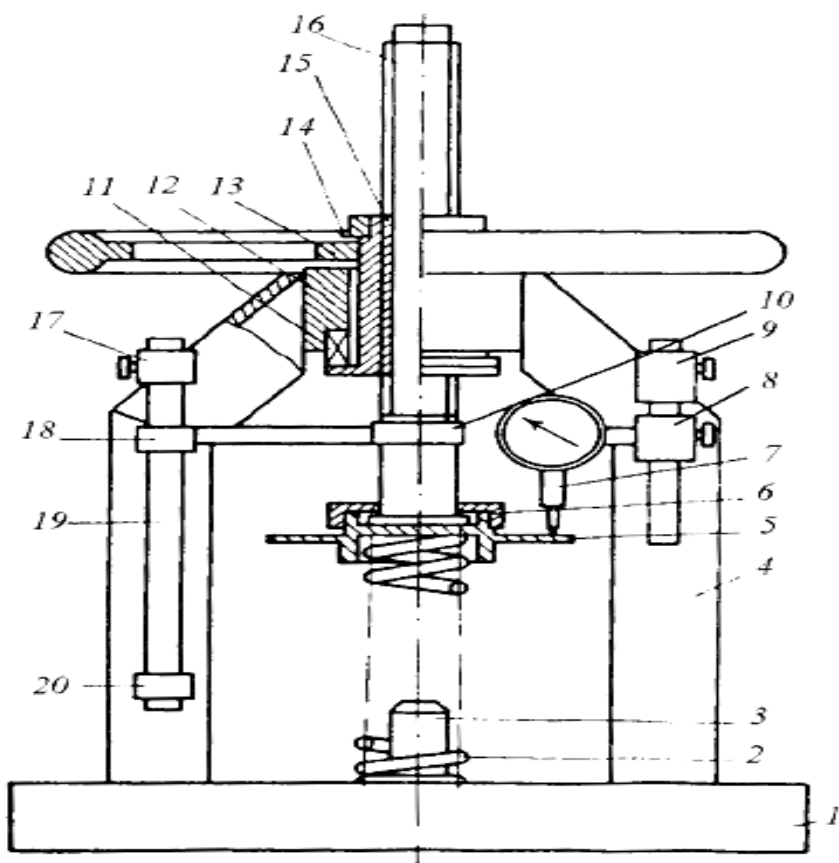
Приспособление для испытания пружин предохранительных клапанов:
